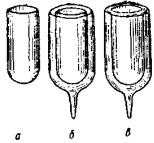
Изготовление дьюаровского спая приемом закатывания наружного цилиндра на внутренний: а —внутренний стакан; б—закатывание наружного цилиндра на внутренний; в—готовый спай.
